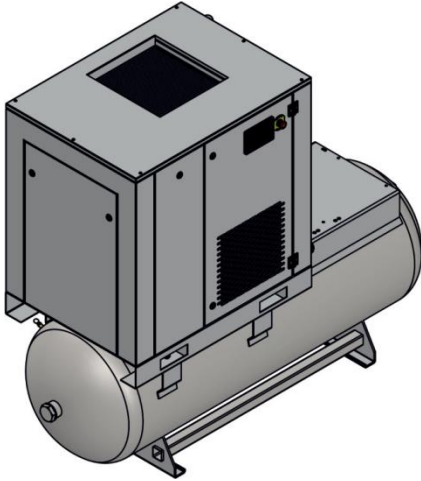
Vedere frontală a compresorului SKTG 11 SXP
